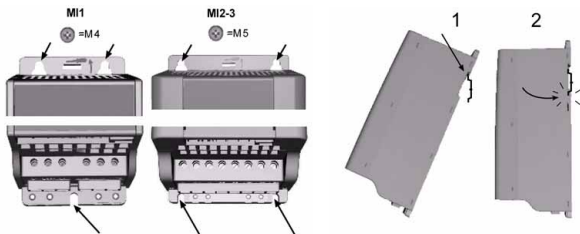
Vissage (gauche) et montage sur rail DIN (droite)
